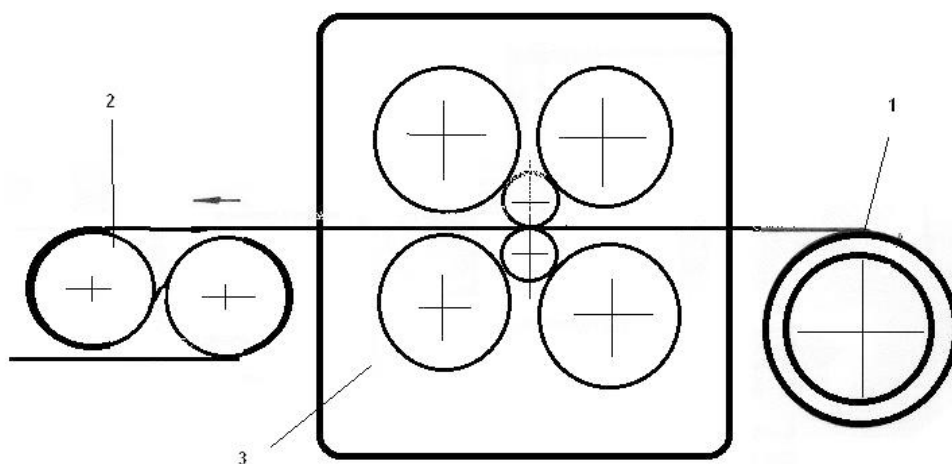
Кинематическая схема калибрующего агрегата: 1 – разматыватель, 2 – клеть дуо, 3 – калибрующий блок.
